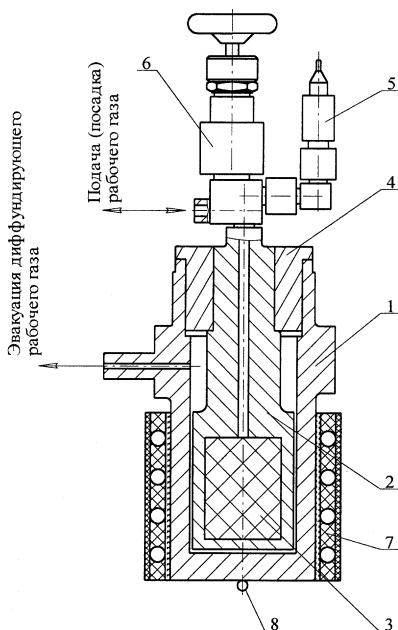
Схематическое изображение источника: 1 – корпус наружный; 2 – корпус внутренний; 3 – металлогидрид (носитель рабочего газа); 4 – герметизирующая крышка; 5 – датчик давления; 6 – вентиль высокого давления; 7 – нагреватель; 8 - термопара
